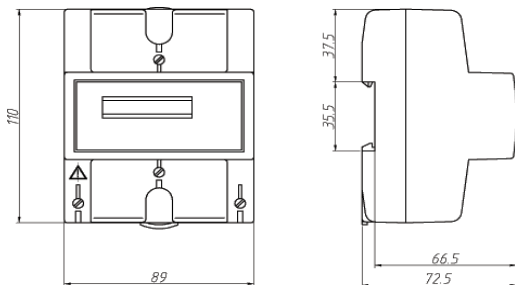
Загальний вигляд лічильника CE102-U в корпусі R5
